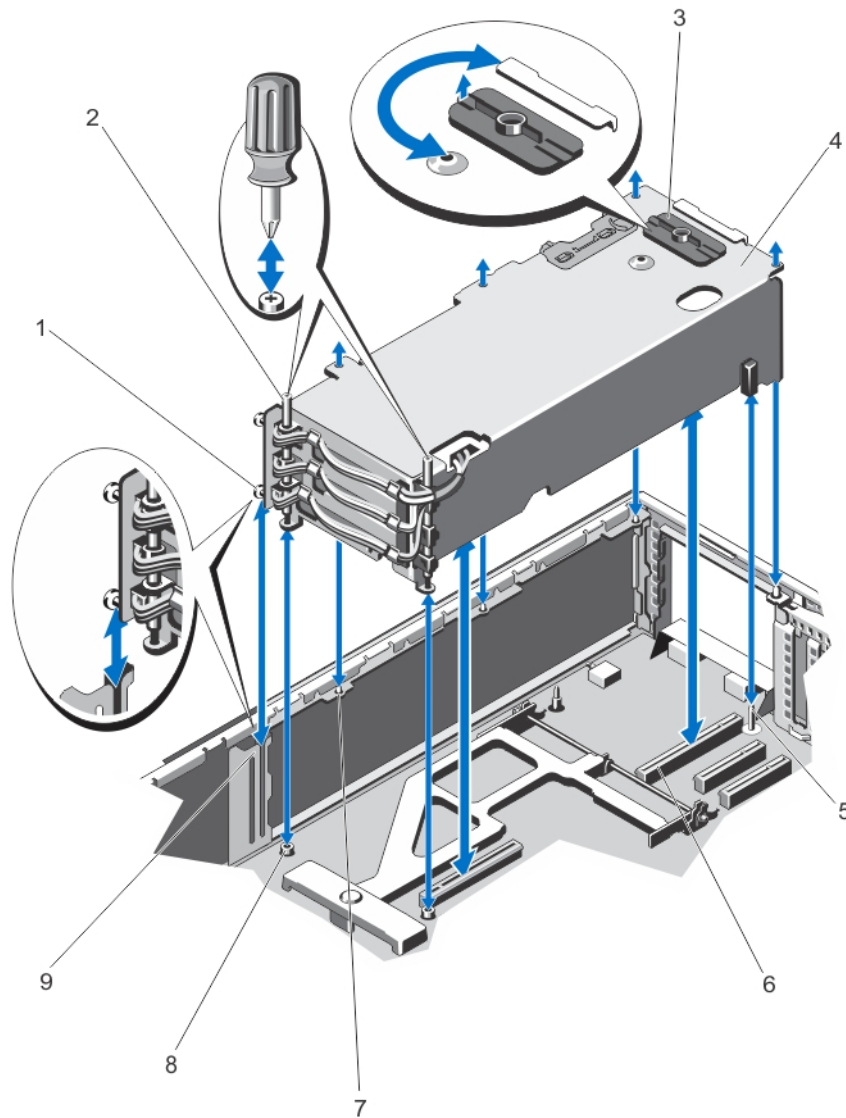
Entfernen und Installieren des PCIe-Gehäuses
